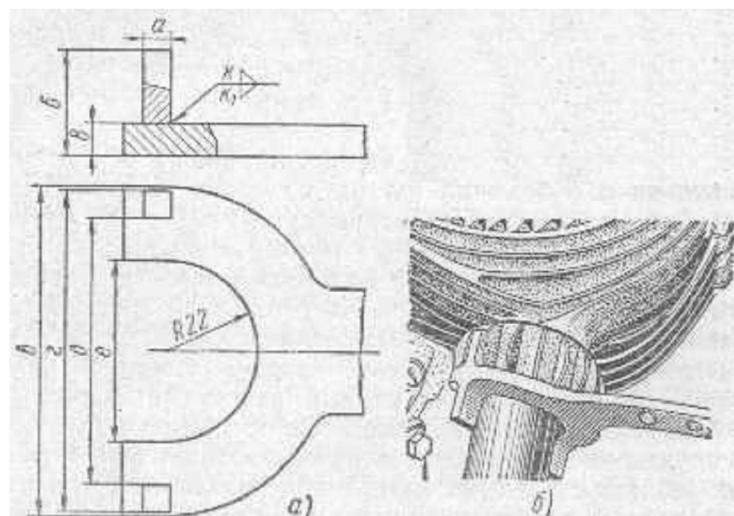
Ключ для гаек крепления выпускной трубы к цилиндрю:
